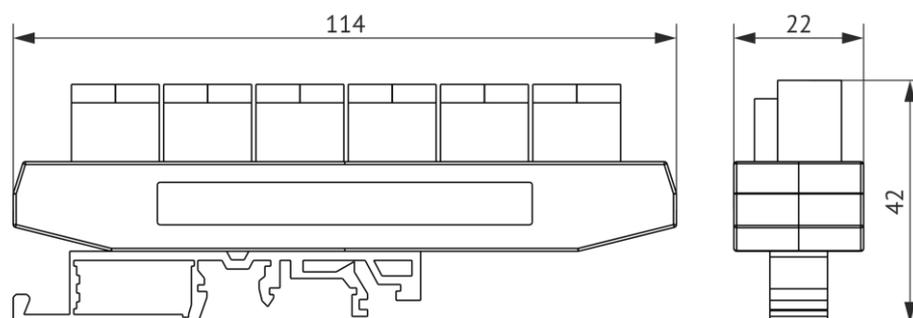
Габаритные размеры EX6RJ, EX6RJS
